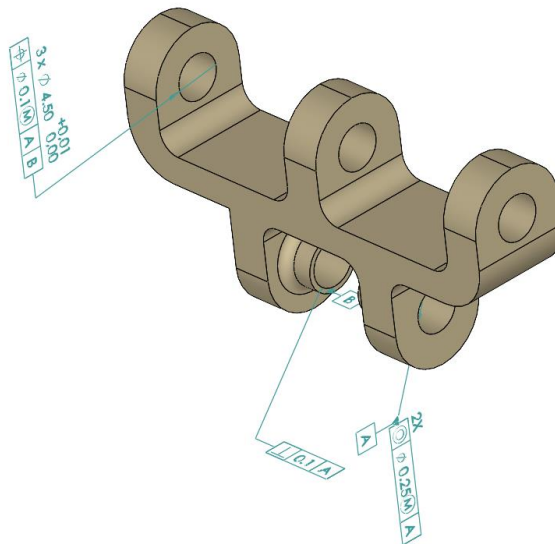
Tolerancias geométricas “Unión Biela-Actuador”
